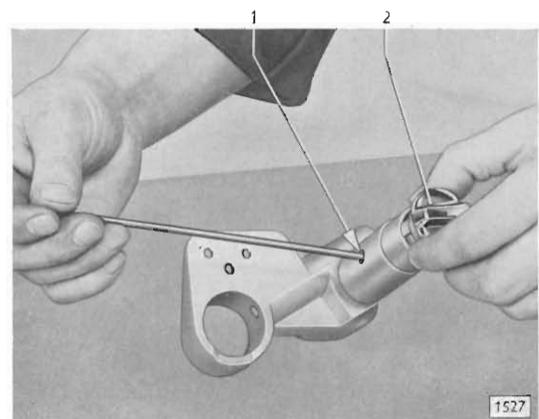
Schließzylinder aus Lenk- und Zündschloß ausbauen (am ausgebauten Schloß in Einbaulage dargestellt)
